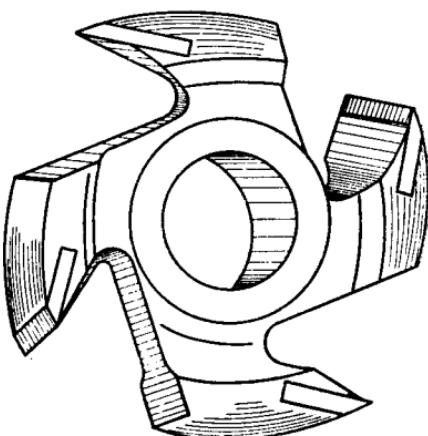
Конструкция фрезы с пластинками из твердых сплавов
